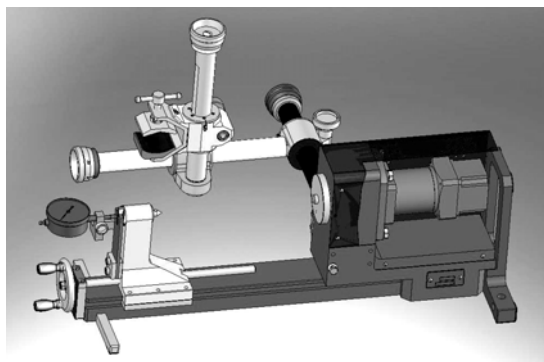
Сварка на поворотном приспособлении с горизонтальной осью вращения
